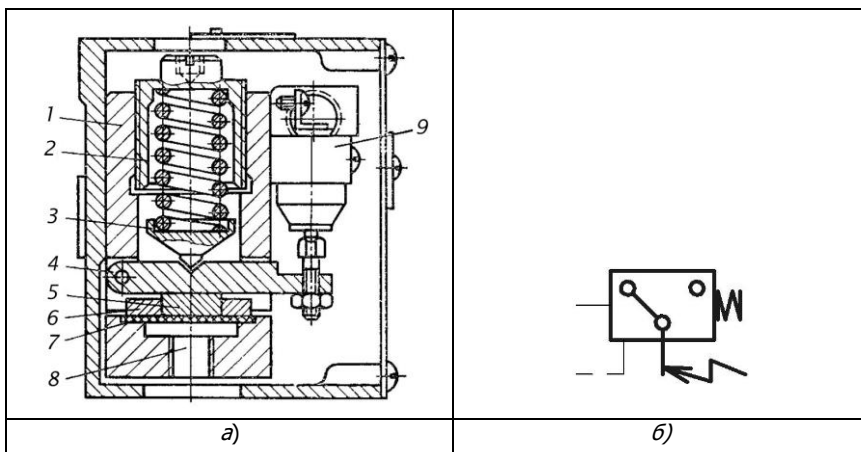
Реле давления Г62-2: а – конструкция; б – условное обозначение
